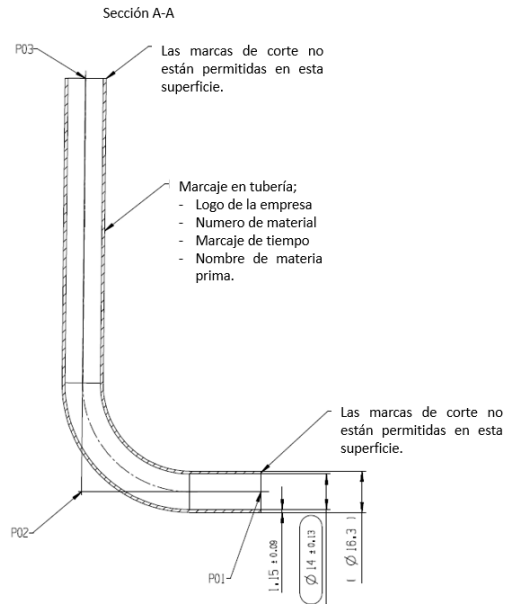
Dibujo 2D de la tubería a la que se le diseñara el molde de ULTEM
